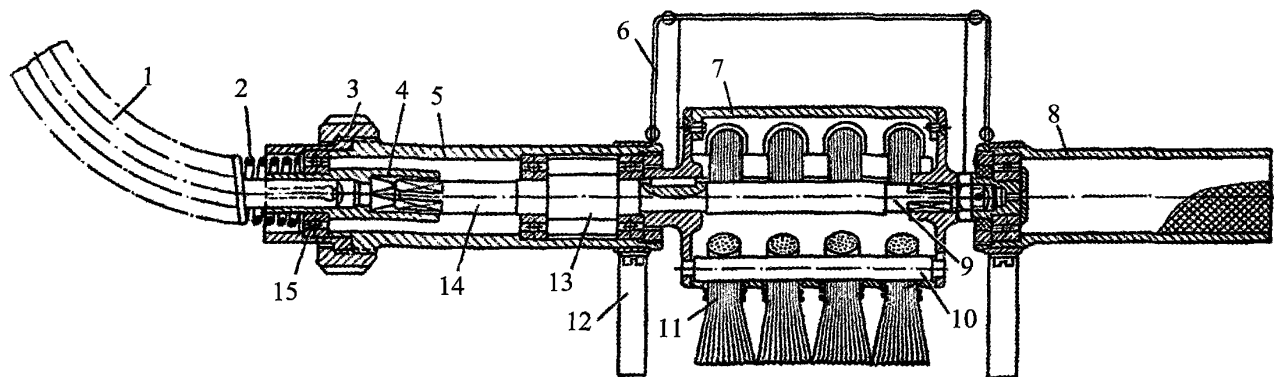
Схема конструкции ударно-центробежной машинки для очистки поверхностей от ржавчины и краски
